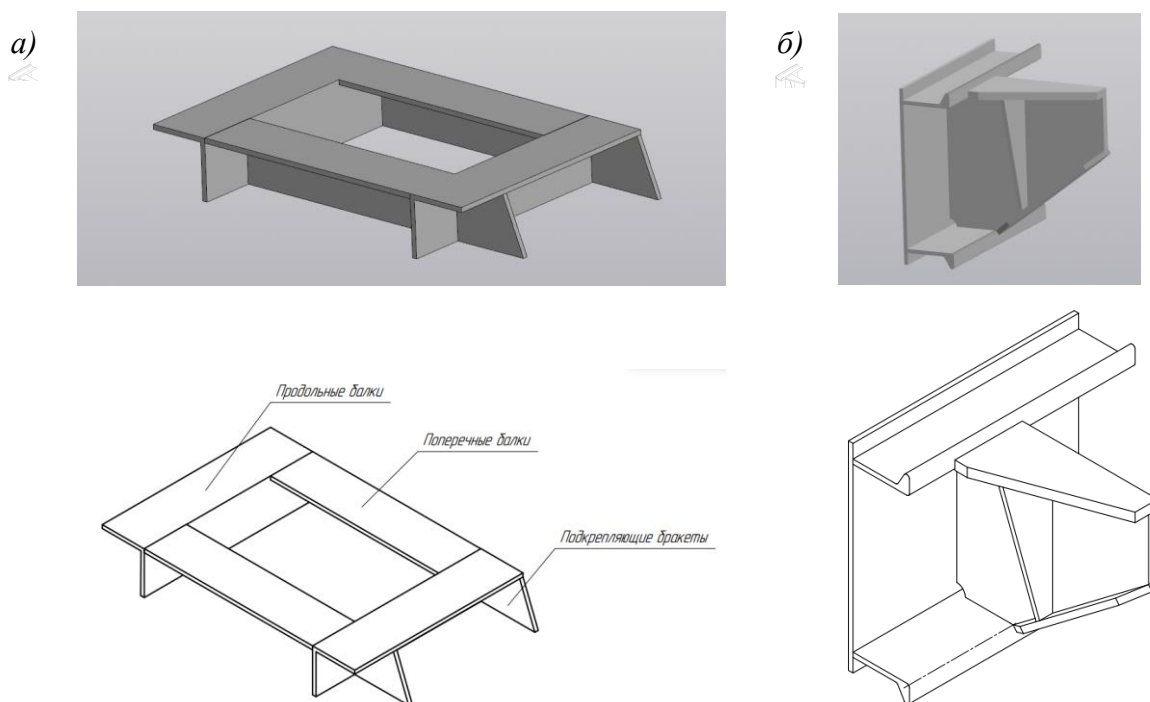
Пример конструкции фундаментов: а – фундамент-стол, б – фундамент-кронштейн
